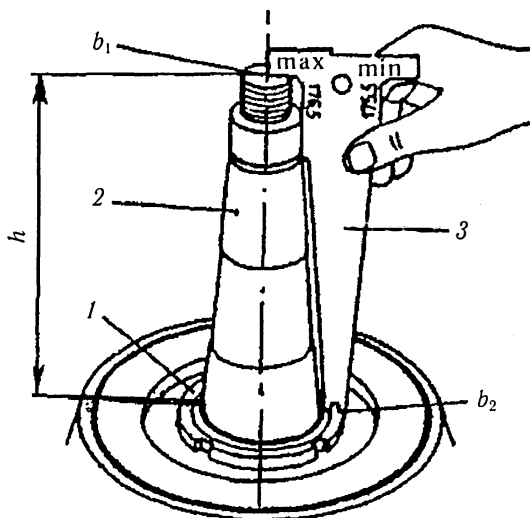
Проверка положения напорного диска по высоте  $h$  относительно верхнего конца вала: 1 — затяжная гайка; 2 — вал; 3 — шаблон;  $b_1$  — верхний зазор;  $b_2$  — нижний зазор
